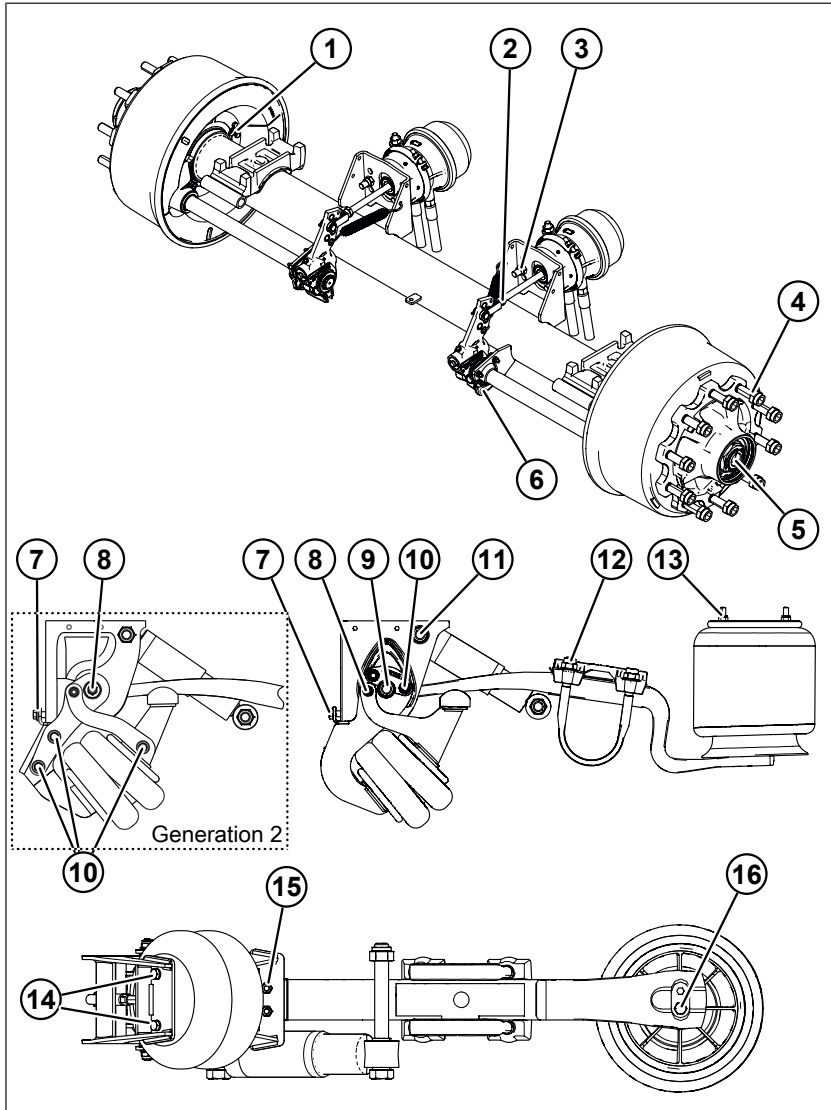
Vue d'ensemble des couples de contrôle et de serrage (bras de suspension pneumatique supérieur)
